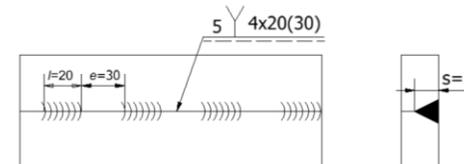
Dimensión transversal de una soldadura en ángulo
